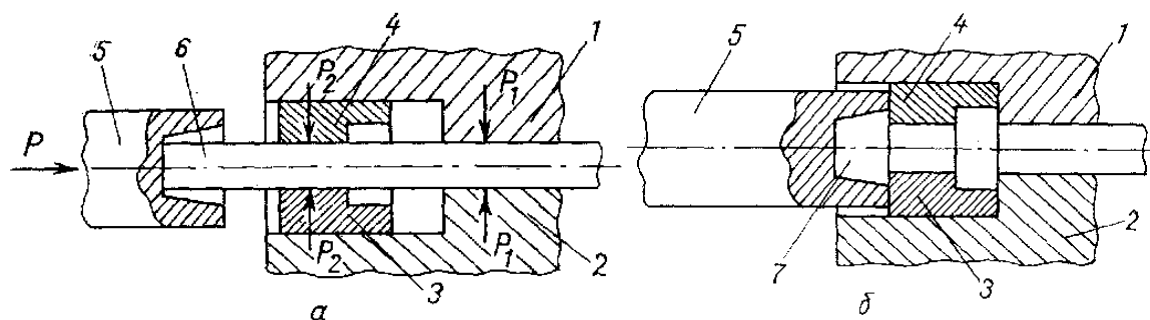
Схема висаджування на ГKM на початковій (а) та кінцевій (б) стадіях: 1, 2 – частини рознімної матриці; 3, 4 – частини додаткової рознімної матриці; 5 – пуансон; 6 – вихідна заготовка; 7 – поковка
